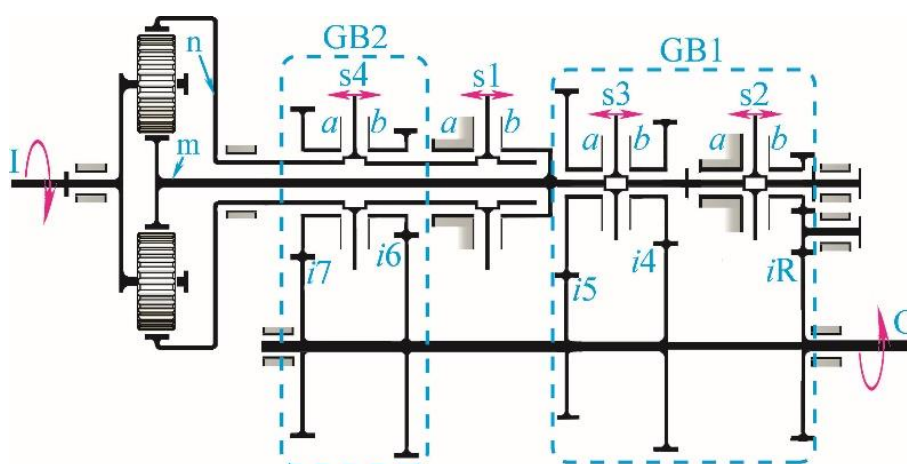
Кинематическая схема 12-ти ступенчатой двухпоточной коробки передач DO.
